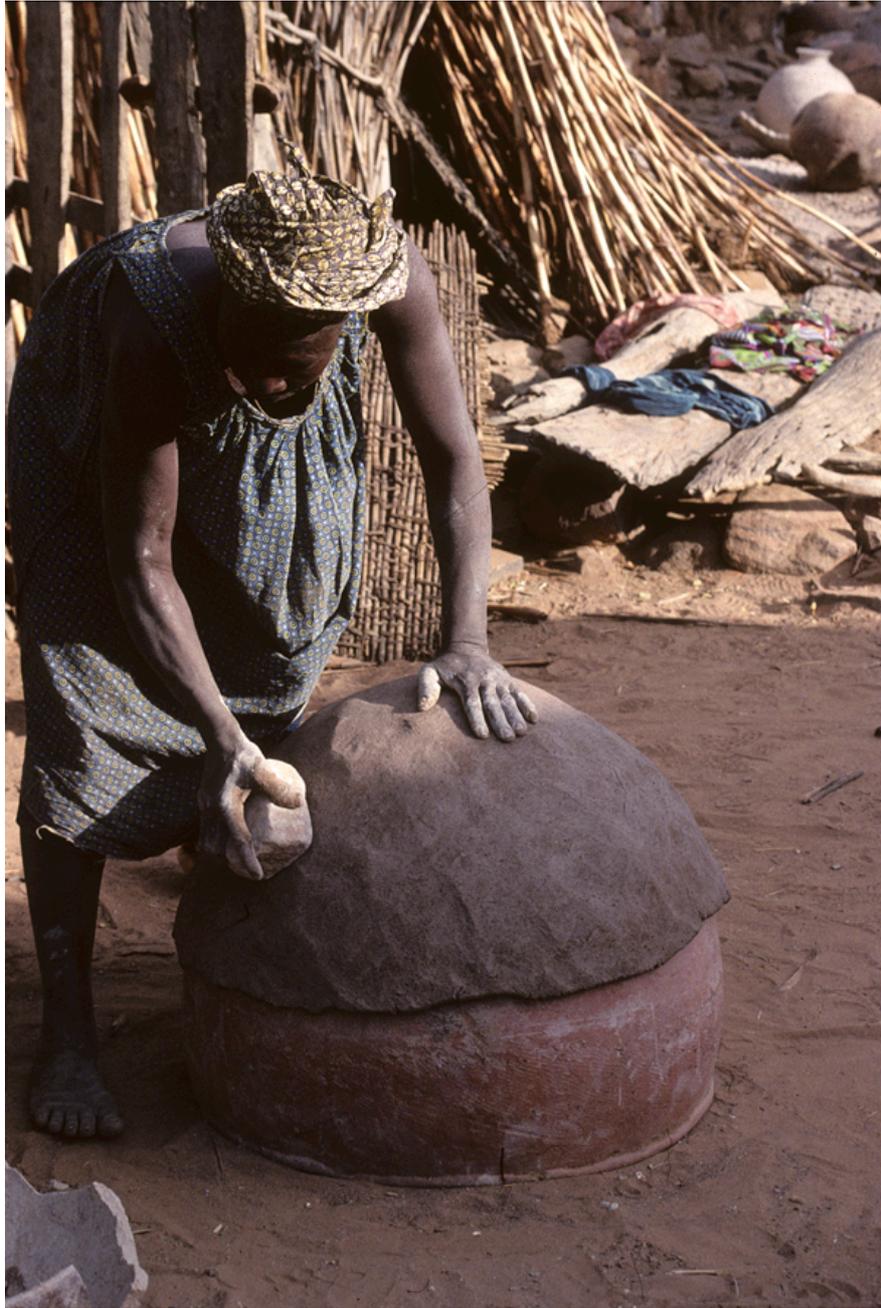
Tradition C1. Yélé. M. Djo (Djo). Moulage sur forme convexe. Étape A1. MAESAO 320.18. 4819.1/Po13.
